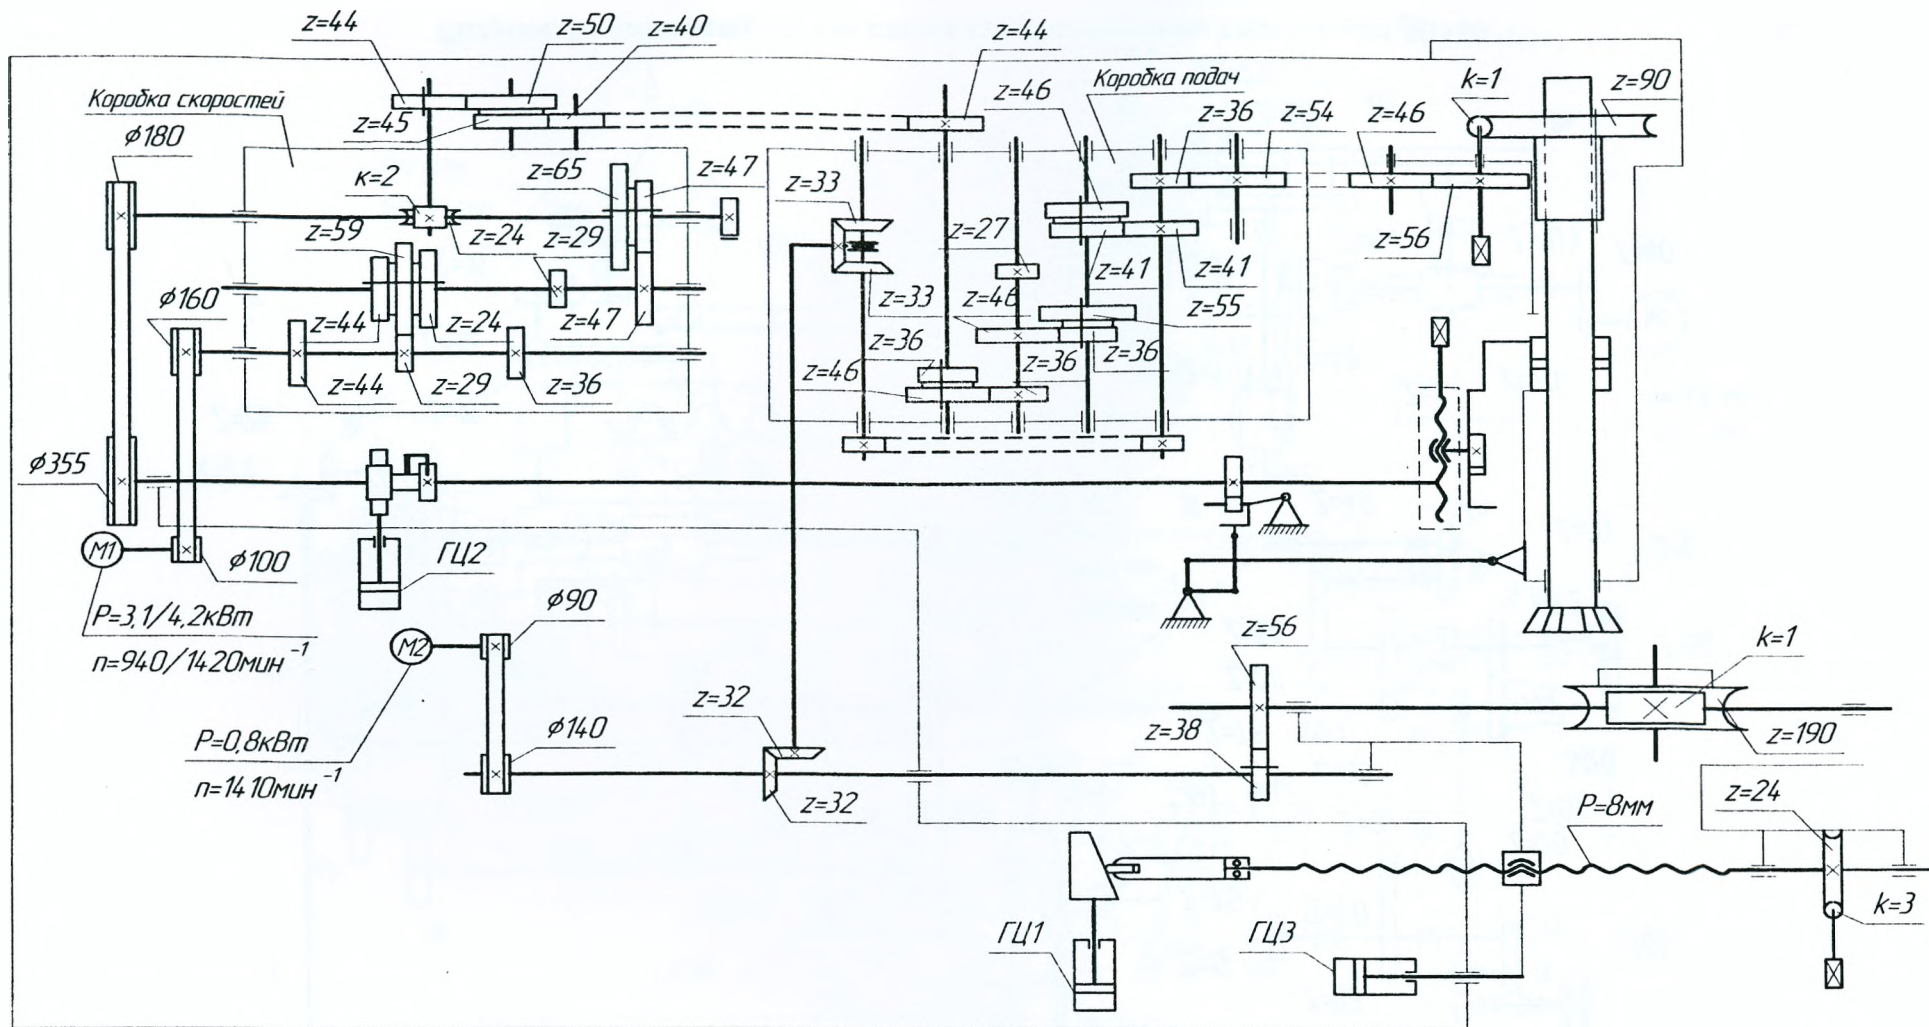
Кинематическая схема зубодолбежного станка мод.5140
